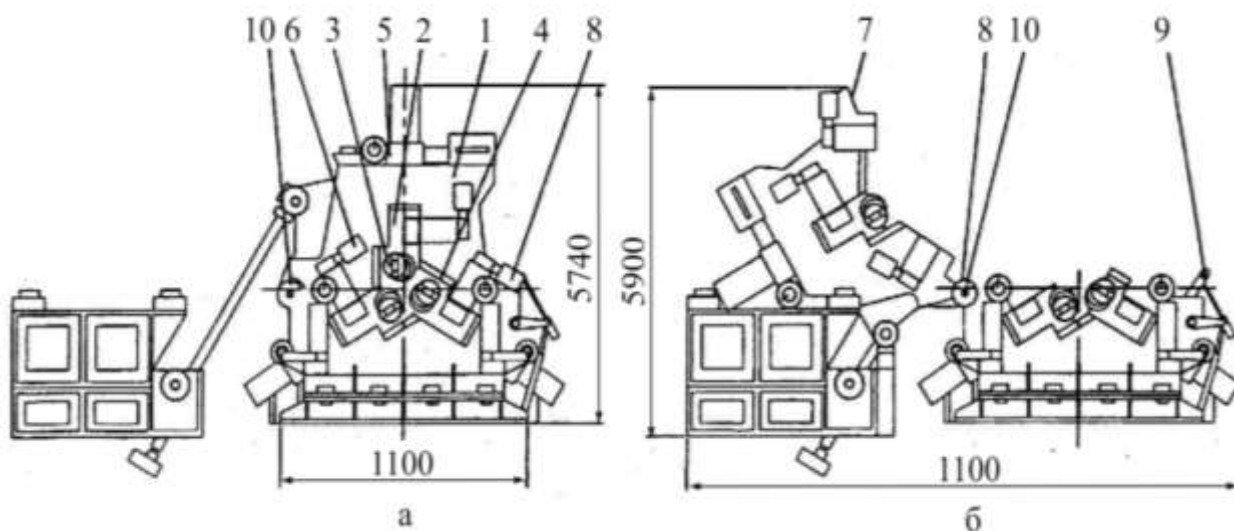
Схема клетки стана СРП-130: а – рабочее положение; б – положение перед перевалкой валков
